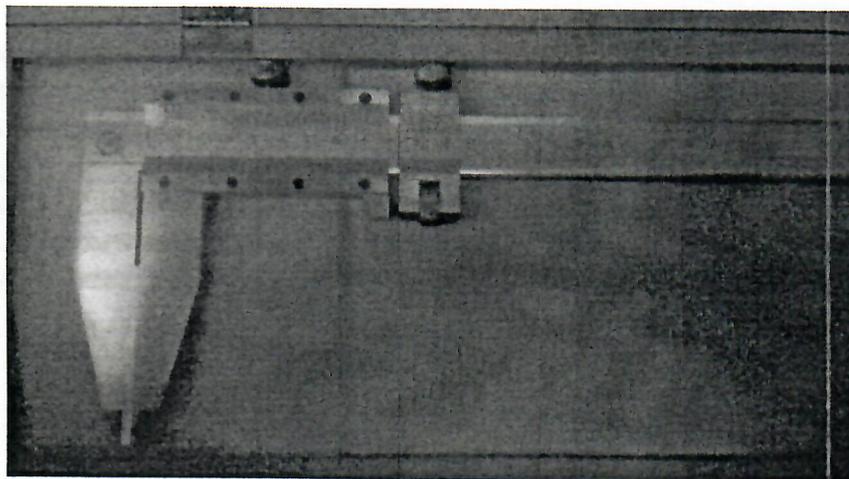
Общий вид штангенциркулей типа IIIЦ-III.
